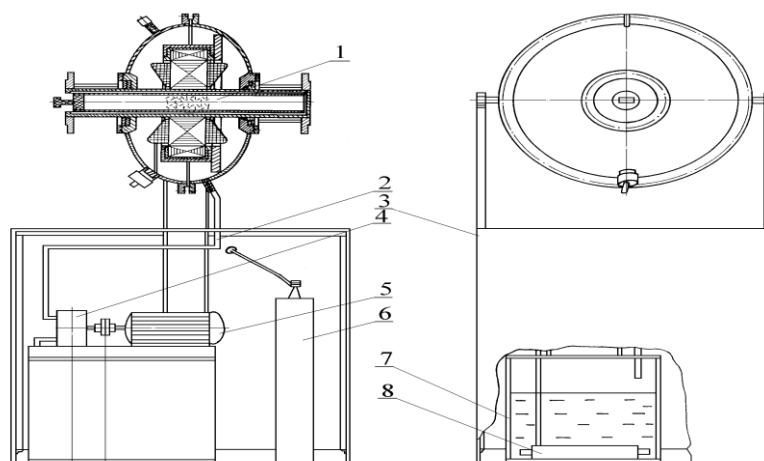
Электромагнитный аппарат для приготовления композиций: 1 – корпус реактора; 2 – шланг; 3 – корпус; 4 – насос; 5 – электродвигатель; 6 – конденсатор; 7 – бак; 8 – холодильник
